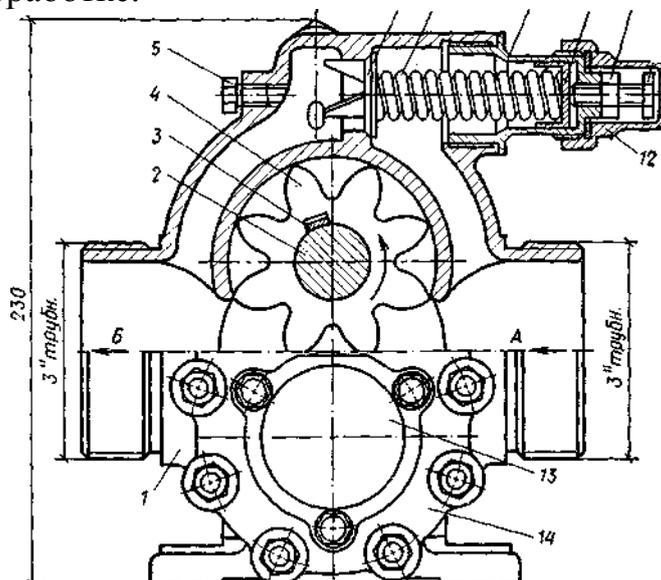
Шестеренный насос НШН-600: 1 – корпус; 2 – вал; 3 – шпонка; 4 – шестерня; 5 – заглушка; 6 – клапан; 7 – пружина; 8 – корпус клапана; 9 – упор; 10 – контргайка; 11 – регулировочный болт; 12 – колпачок; 13 – крышка подшипника; 14 – крышка насоса
